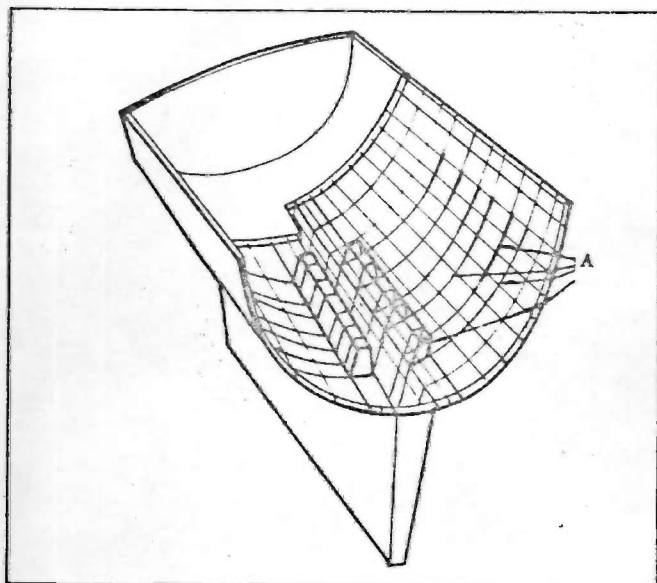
Kielconstructie voor een geballast zeiljacht.
